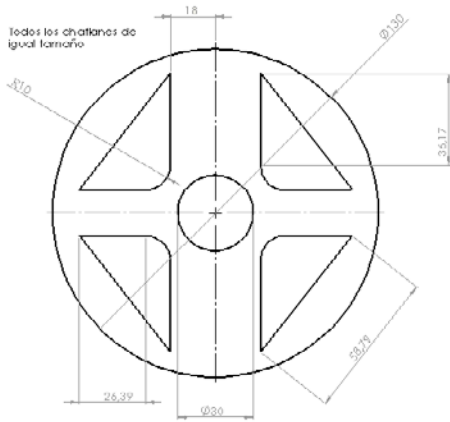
figura construida en MMGS y con un valor de extrusión de 10 milímetros y la pieza se realiza en plano planta.
